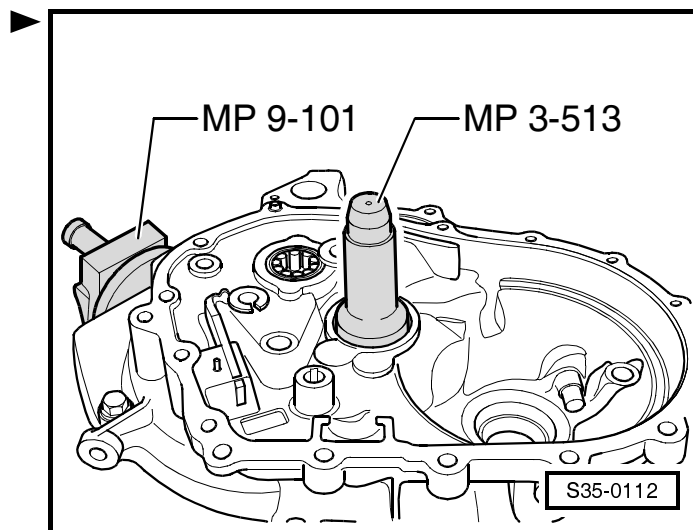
Demontáž válečkového ložiska ze skříně spojky
